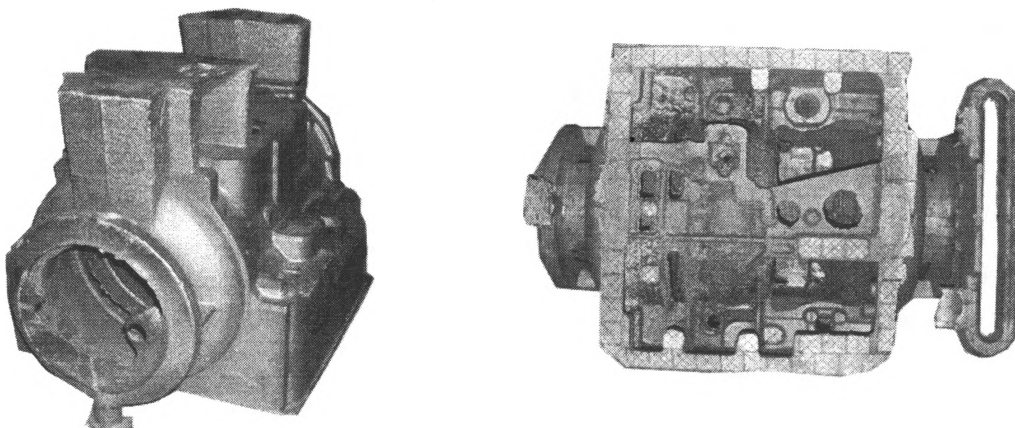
Общие виды отливки «Корпус коробки переключения передач «Фойт»
